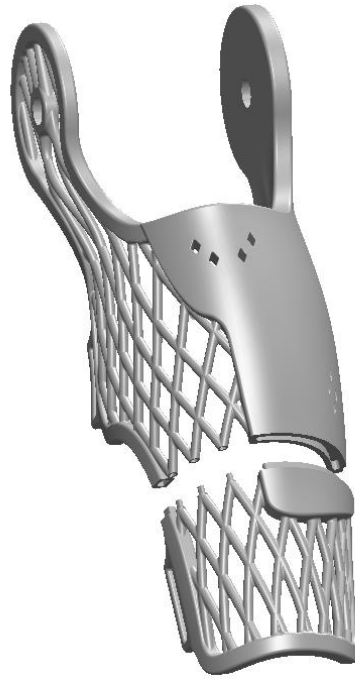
Suddivisione della struttura inferiore per necessità di stampa
